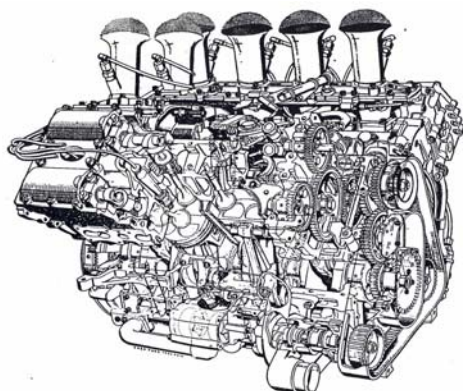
Výkres řezu lodním motorem ČNM- L 350 PN [6]
